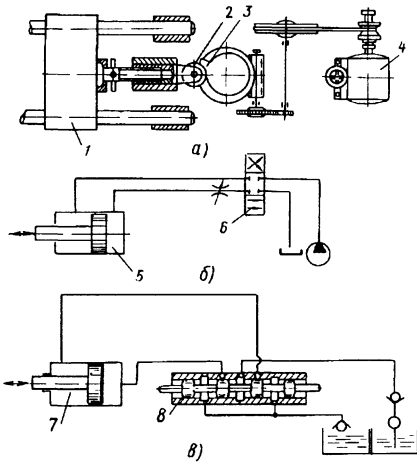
Механизмы сближения стыковых машин для сварки оплавлением:
